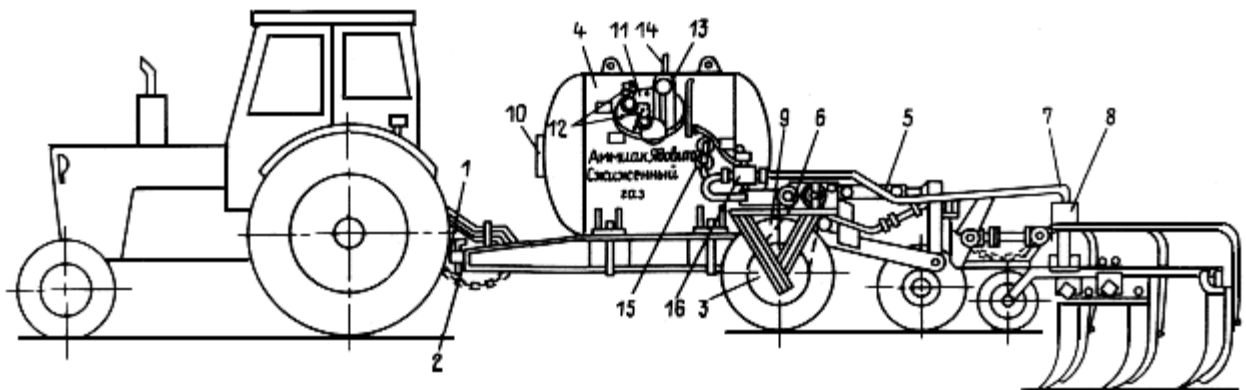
Агрегат АБА-0,5М: 1 - серьга; 2 - предохранительная цепочка; 3 - диск колеса; 4 - цистерна; 5 - механизм задней навески; 6 - насос-дозатор; 7 - клапан отсечной; 8 - распределитель; 9 - цепная передача; 10 - уровнемер; 11 - крышка люка; 12 - вентили; 13 - манометр; 14 - предохранительный клапан; 15 - расходный вентиль; 16 - теплообменник
